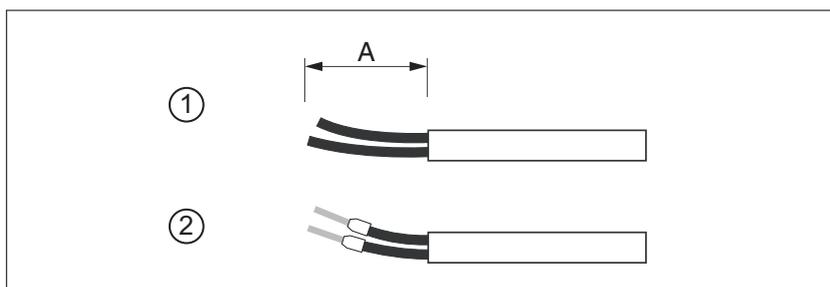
Assemblaggio dei cavi del ventilatore
